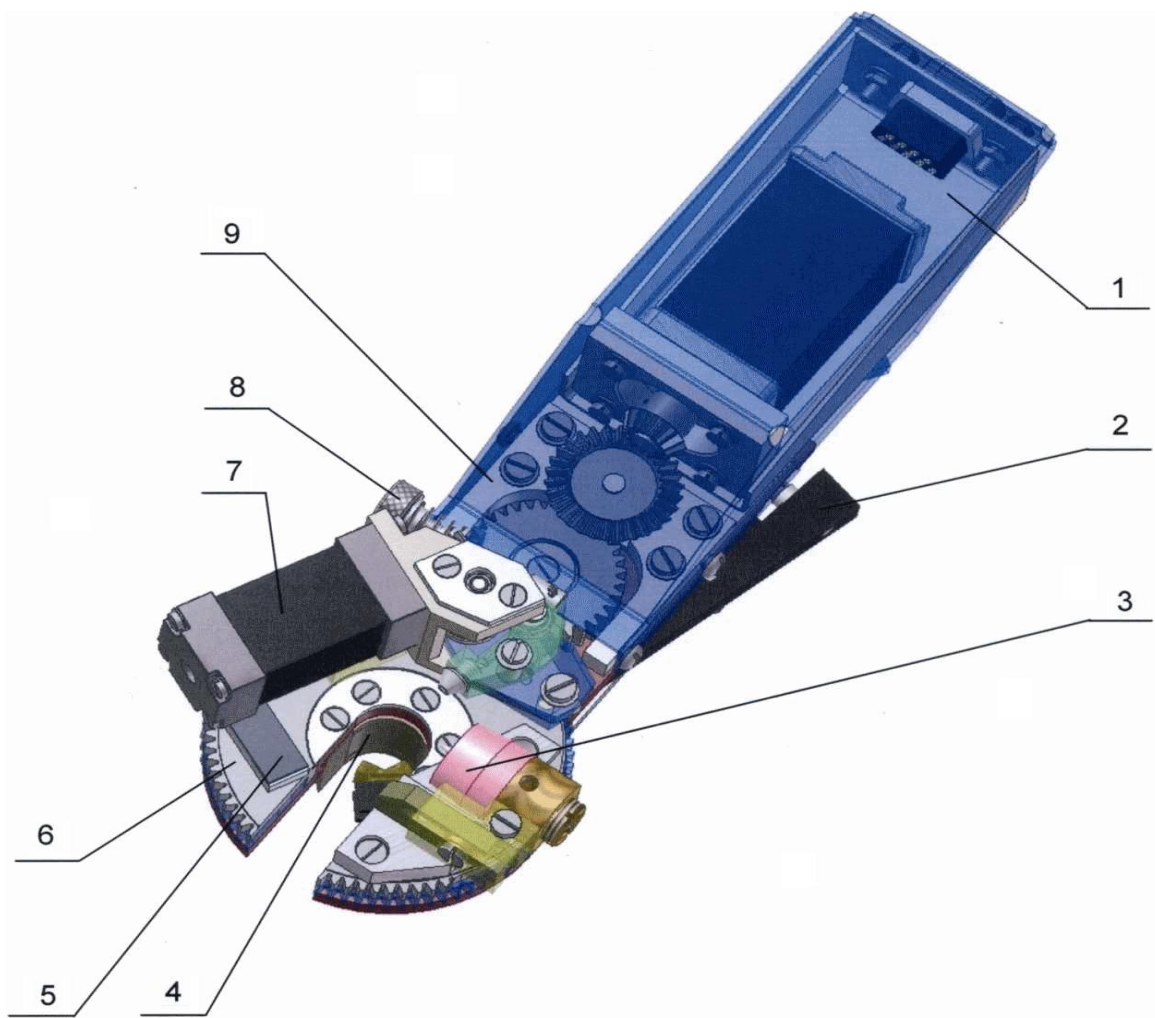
Конструкция сварочной головки ГНС 14
